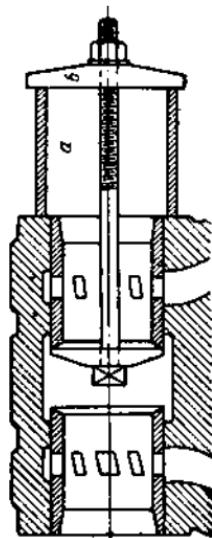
Приспособление для запрессовки гильз и выпрессовки гильз.
